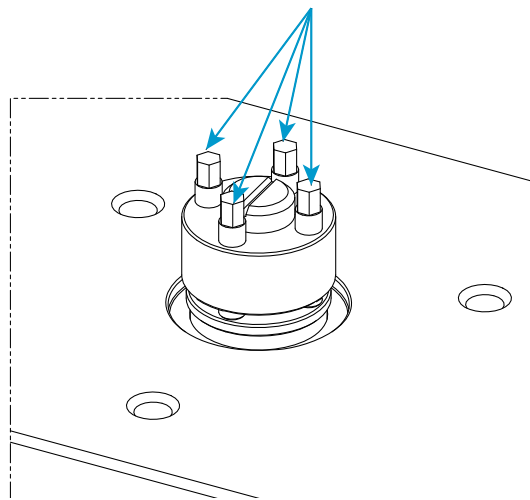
Mechanische Spannvorrichtungsbaugruppe
